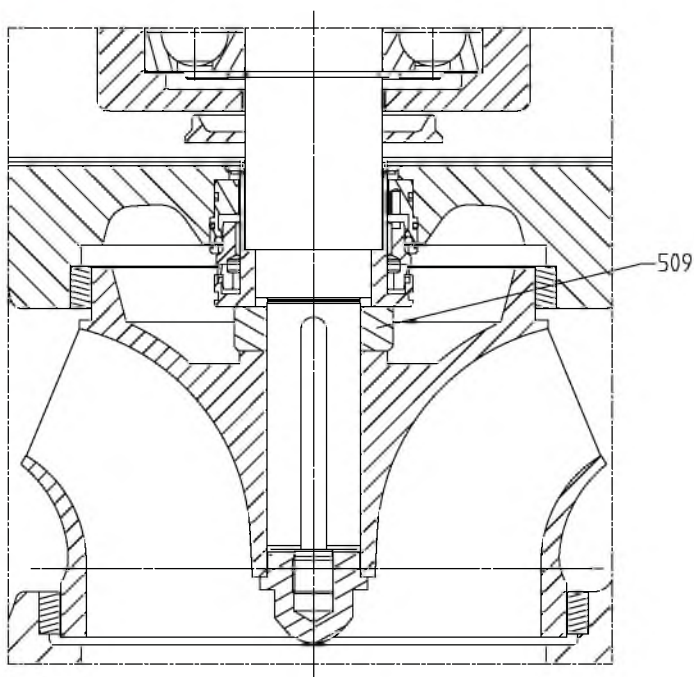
Исполнение с промежуточным кольцом (только для типоразмеров 250-250, 250-300, 350-340)
